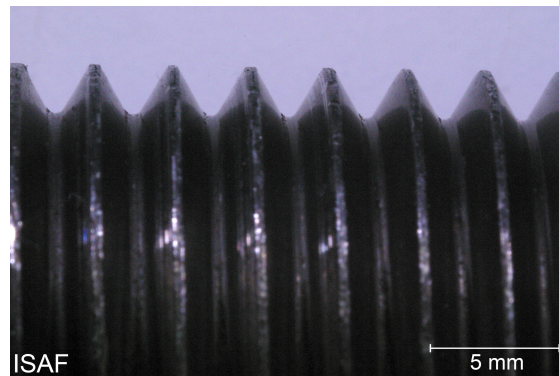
Gewindeprüfkörper axial belastet mit 10kN (Bolzen)
